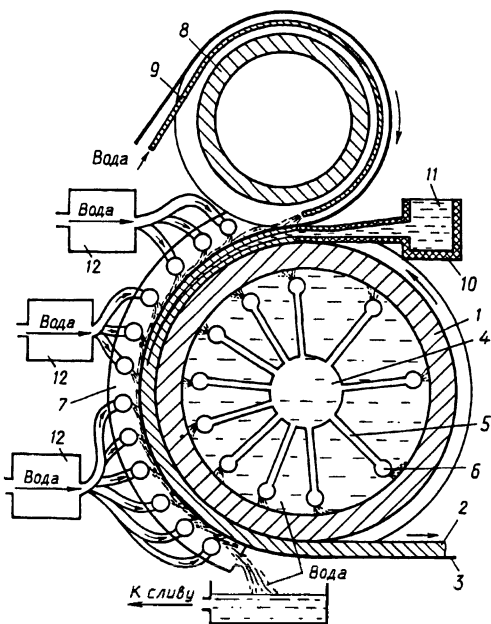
Схема охлаждения кристаллизатора: 1 — колесо; 2 — отливка; 3 — рабочая лента; 4 — коллектор; 5 — труба питающая; 6 — спрейер; 7 — охладитель ленты; 8 — валок прижимной; 9 — трубка верхнего охлаждения; 10 — распределитель расплава; 11 — расплав; 12 — ресиверы
